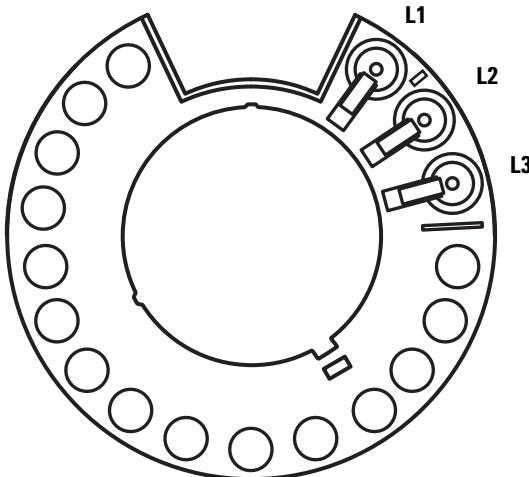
Posizioni L1, L2, L3 della torretta di trasferimento (vista dall'alto)
